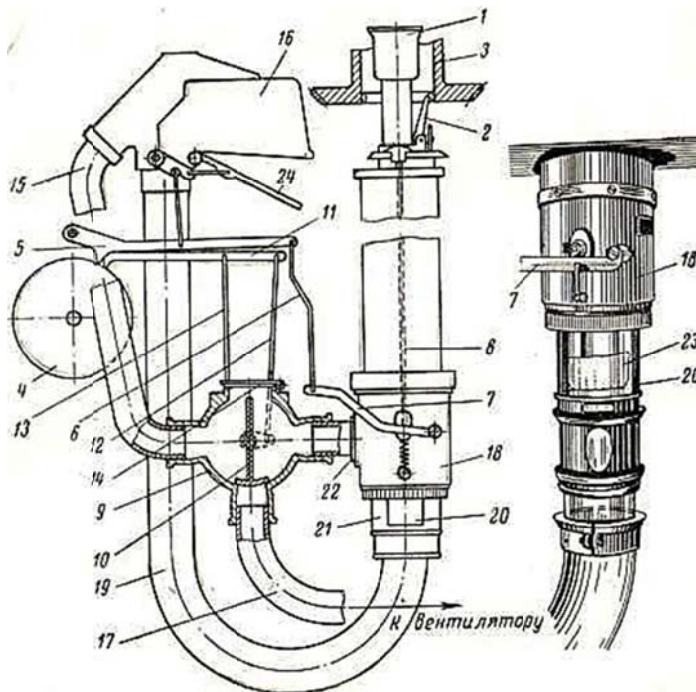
Механизм пневматической оттяжки с автоматической вывороткой изделия
